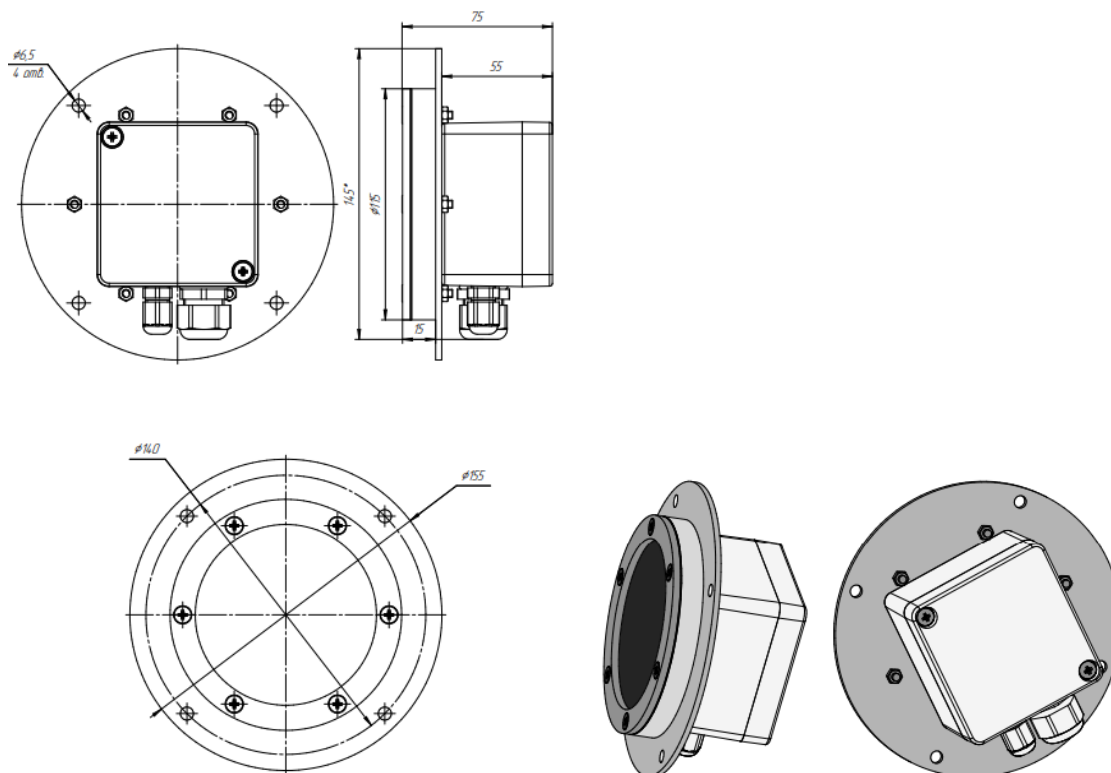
Габаритные и присоединительные размеры ДЗ исп.00
